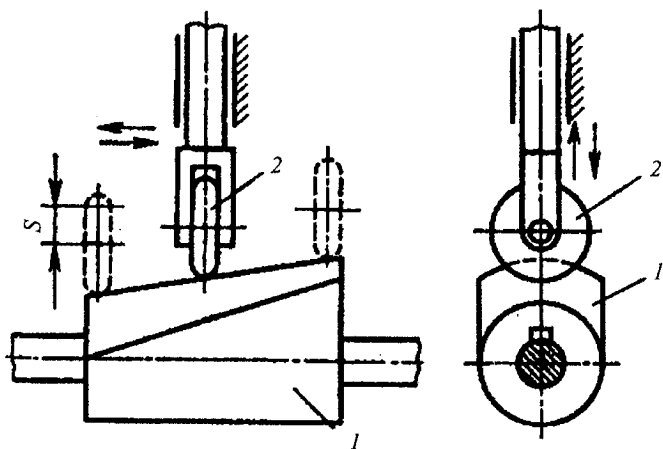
Циліндричний кулачковий механізм із змінною висотою кулачка 1:
